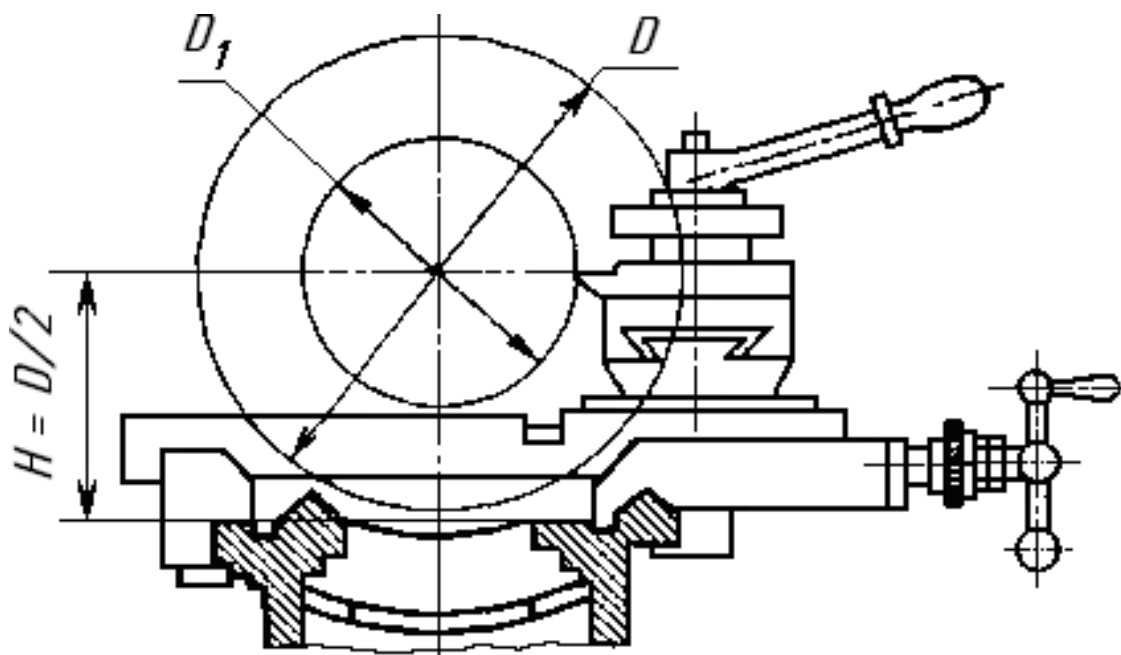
Габариты обрабатываемых на станке заготовок
